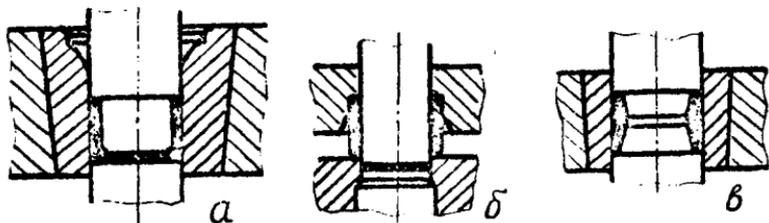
Схема технологического процесса изготовления втулок методом глубокой вытяжки стаканов с последующей пробивкой дна и формовкой конусных поверхностей: а - вытяжка стакана; б - пробивка дна; в - формовка конических поверхностей.
